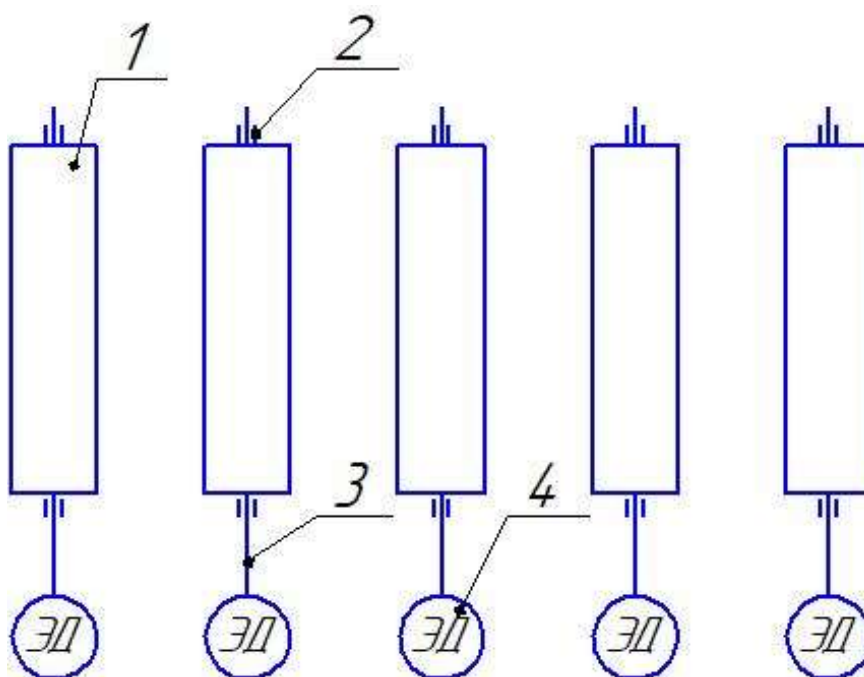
Кинематическая схема привода одной части транспортного рольганга
